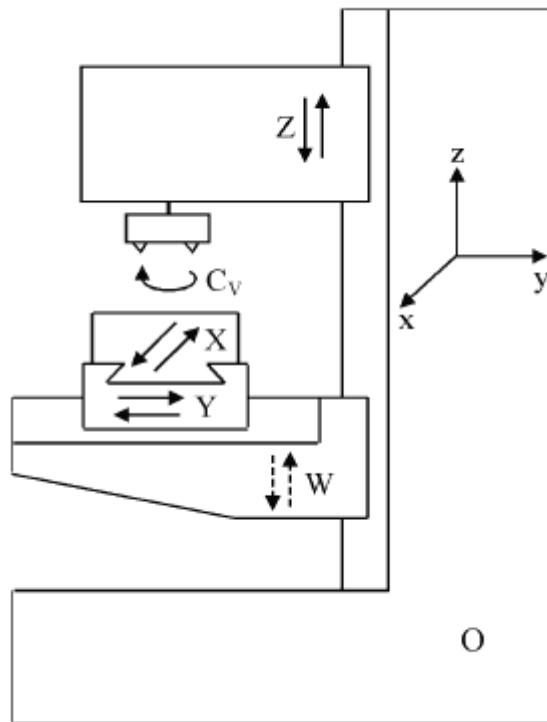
Компонувальна схема вертикально-фрезерного верстата - $XYwOZC_v$
